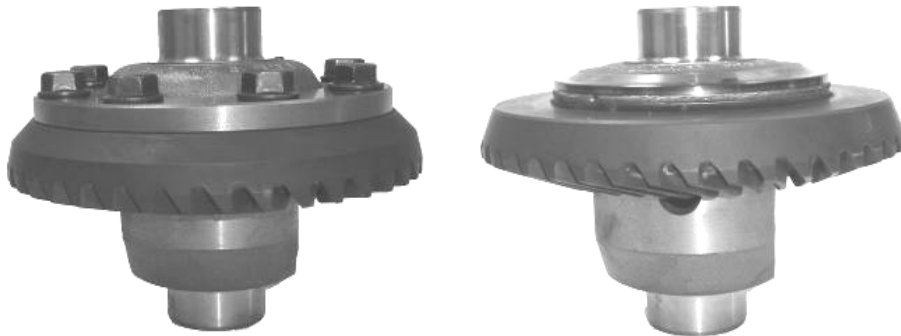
PKW-Achsausgleichgetriebe: geschraubte und geschweißte Version (©BMW AG)
